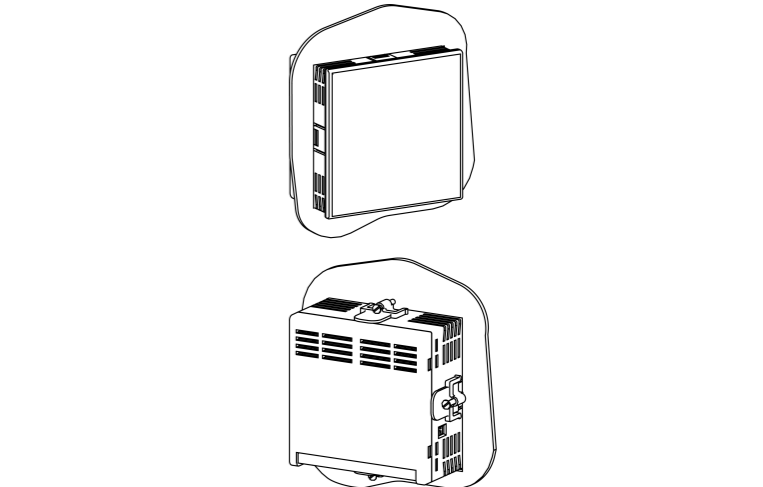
Монтаж прибора щитового крепления Щ1
